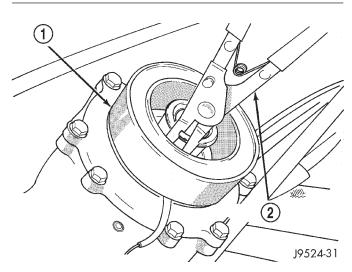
DESMONTAJE DE ANILLO DE MUELLE DE BOBINA DE CAMPO DE EMBRAGUE
